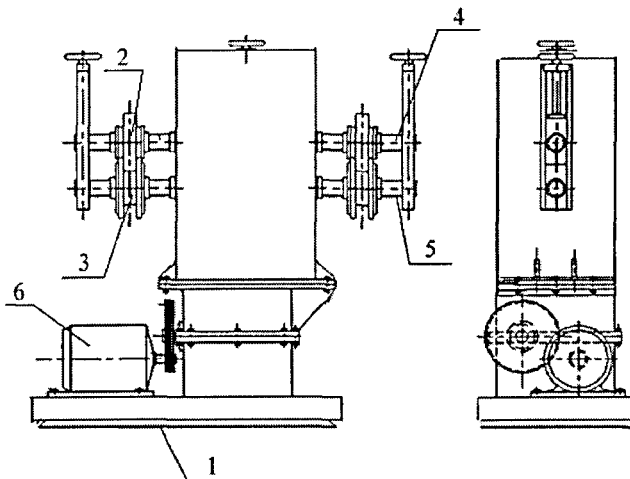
Общий вид модели клетки волоочно-прокатной установки по патенту № 2226441: 1 – основание; 2,3 – ролики формирующие; 4 – верхний вал; 5 – нижний вал; 6 – электродвигатель
